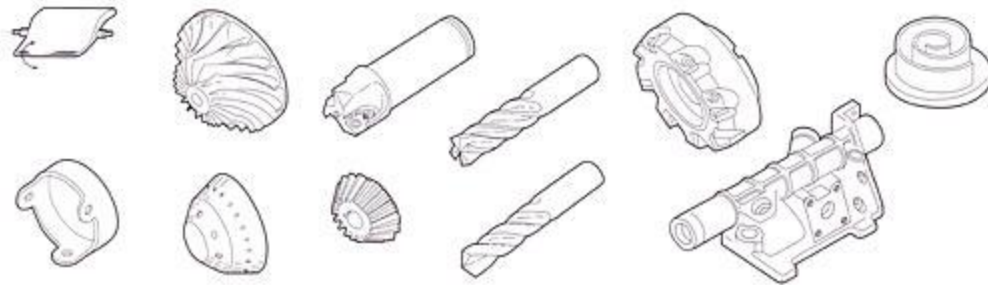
Зразки виробів виготовлені допомогою поворотного столу з ЧПУ
